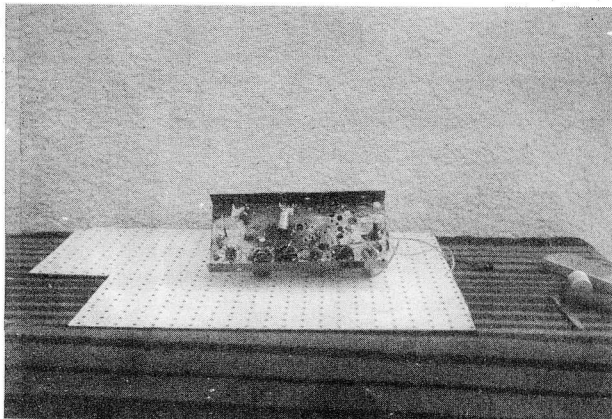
Vue du dessous d'une autre version du montage.
